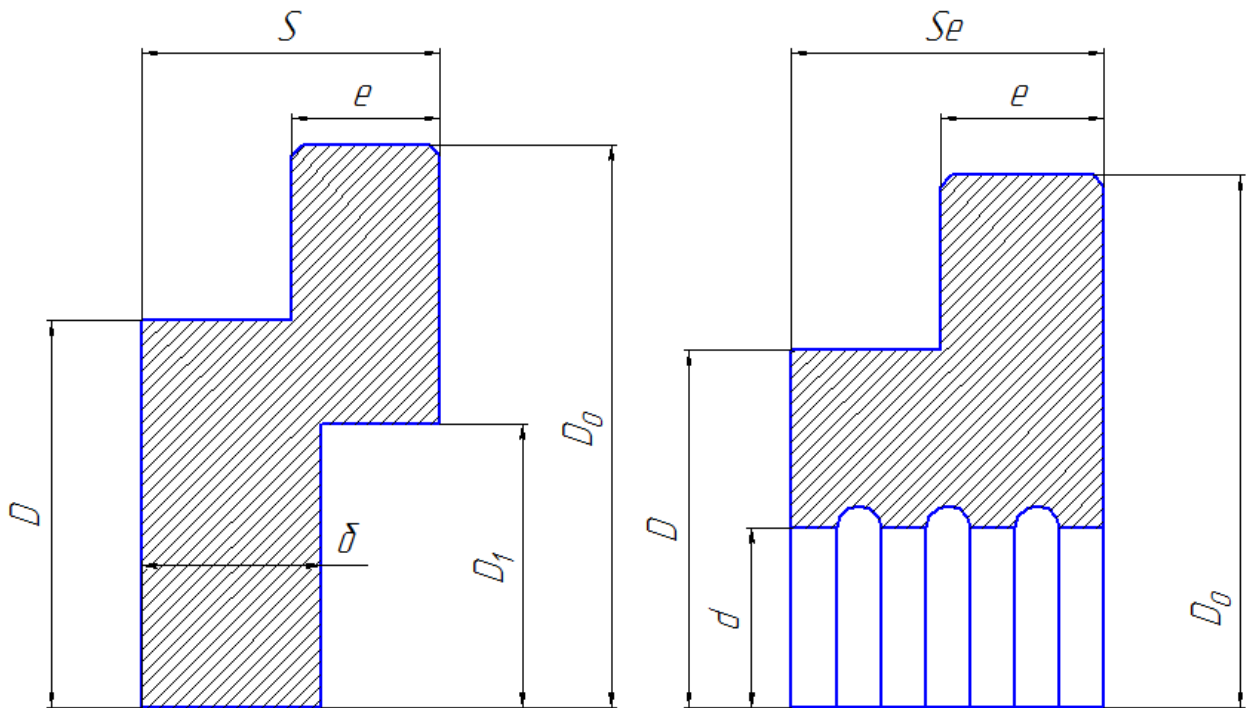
Эскиз крышки закладной глухой. Рис.7.7. Эскиз крышки закладной сквозной со щелевым уплотнением
